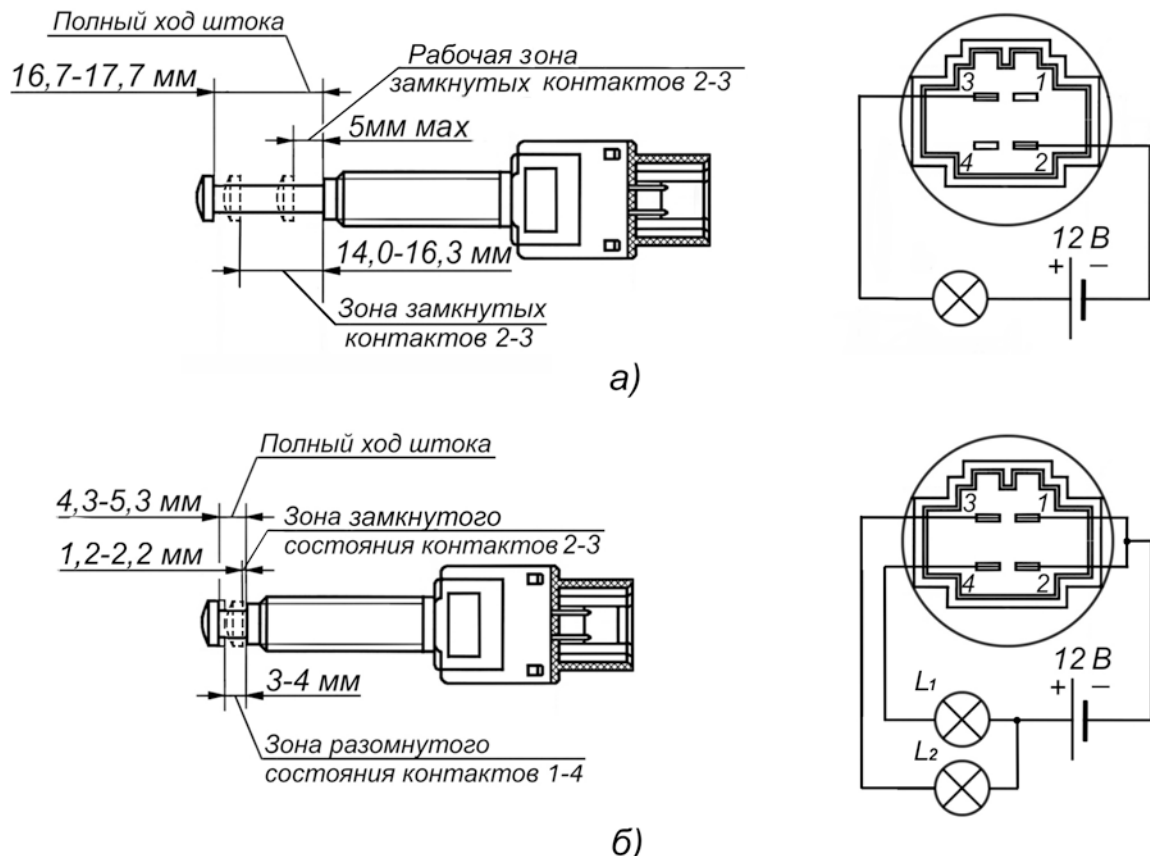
Проверка выключателей: а - выключатель сигнала положения педали сцепления; б - выключатель сигналов торможения
